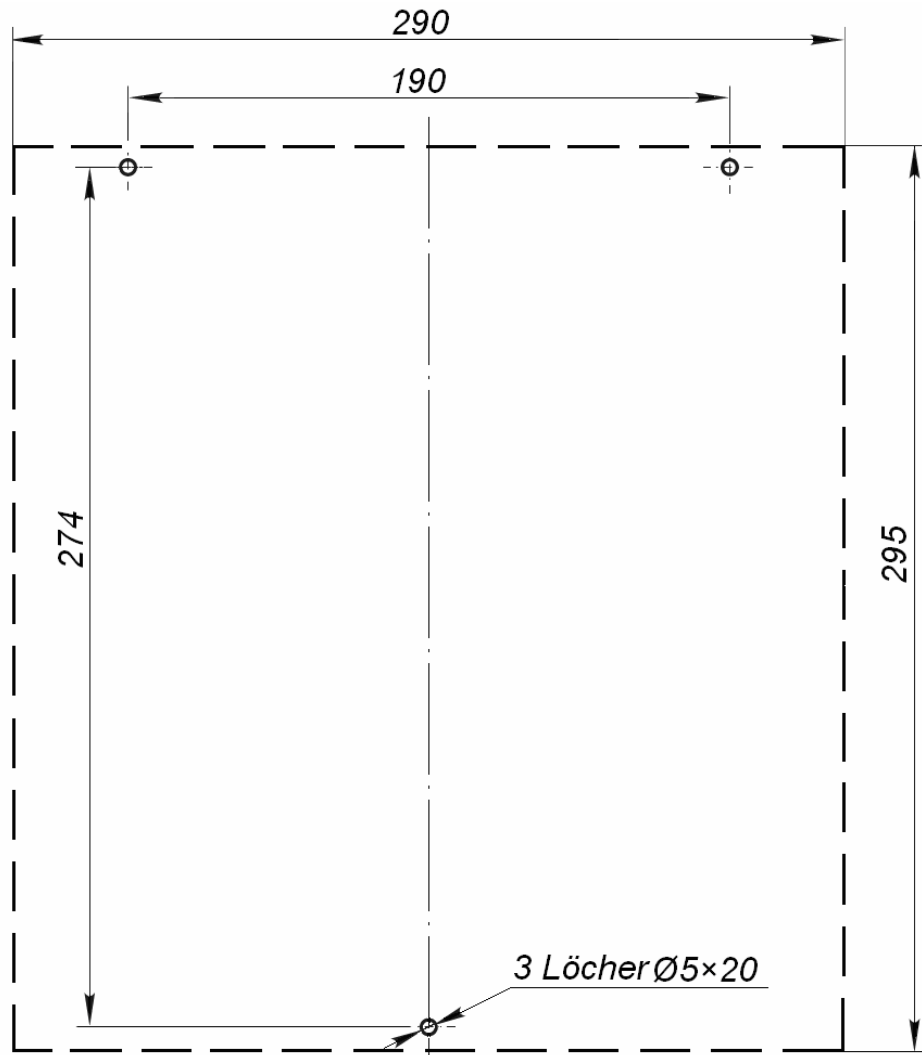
Die Markierung der Öffnungen für die Befestigung des Steuerblocks an der Wand
